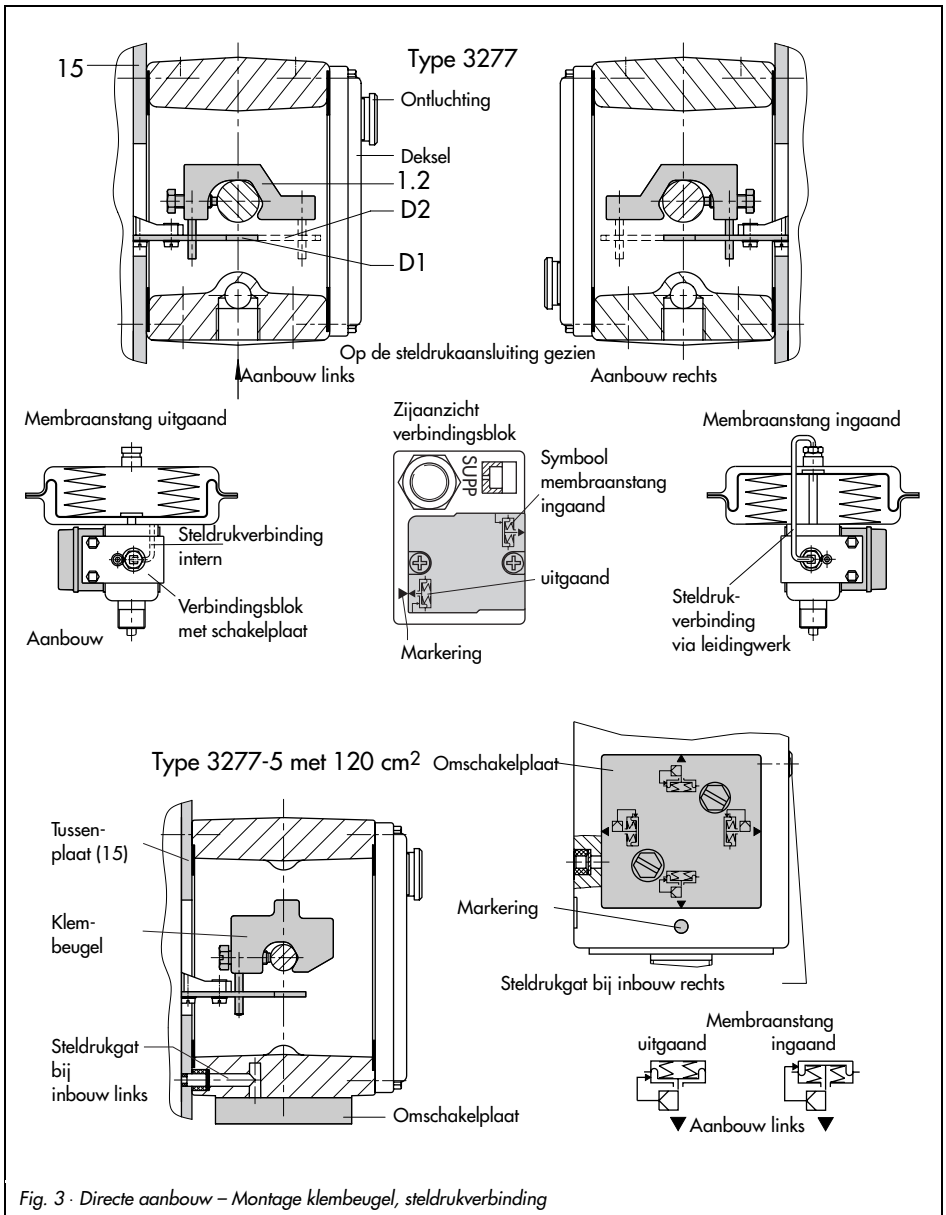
· Directe aanbouw – Montage klembeugel, steldrukverbinding
